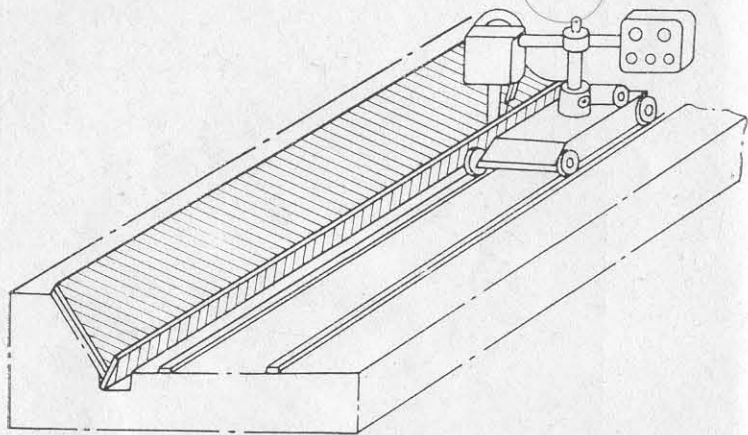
Приспособление для автоматической сварки тавровых узлов «в лодочку».
